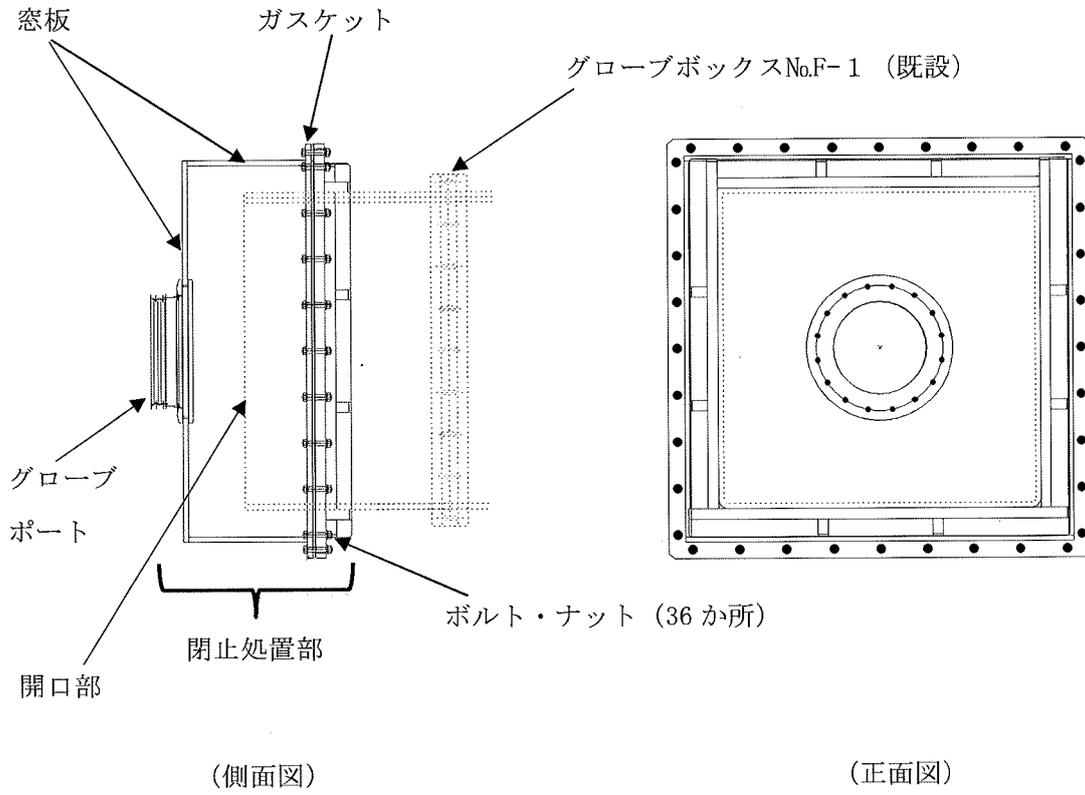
グローブボックス No. F-1 閉止処置部正面図、側面図
